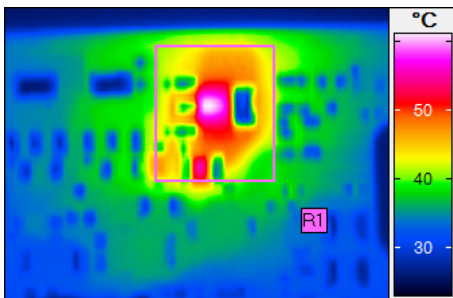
5x Digitalzoom in ein Wärmebild mit Hotspot - PCB
